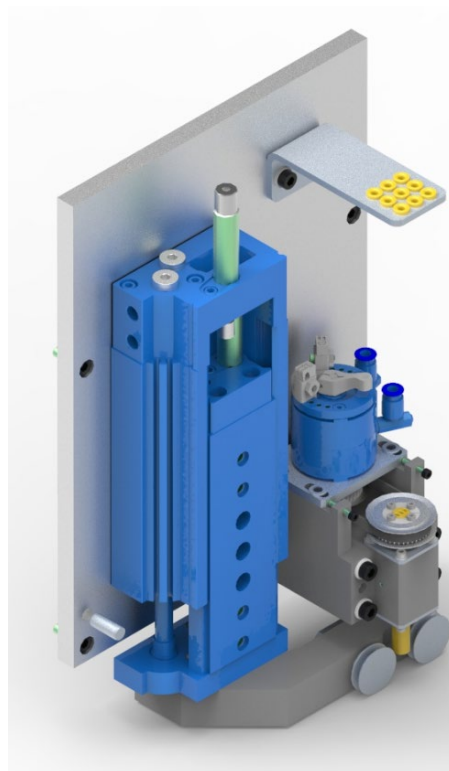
Modul 4 - Einbringen vom Innenwerkzeug in den Stator
